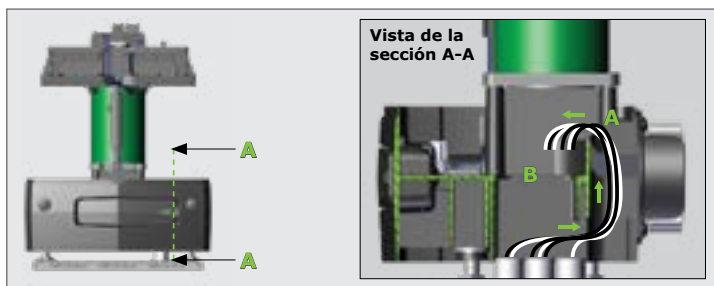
ENRUTAMIENTO DE CABLES PARA RETROAJUSTE CON CABLES M3S LARGOS
